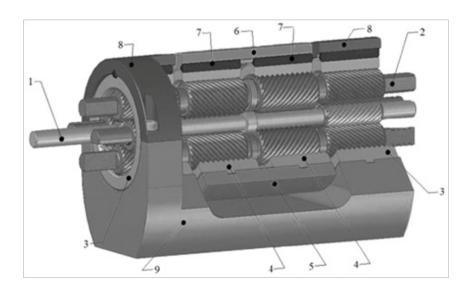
Схема роликовинтового редуктора: 1 – винт; 2 – ролик; 3 – гайка опорная; 4 – гайка выходная; 5 – хомут; 6 – хомут; 7 – шпонка; 8 – хомут; 9 – корпус
